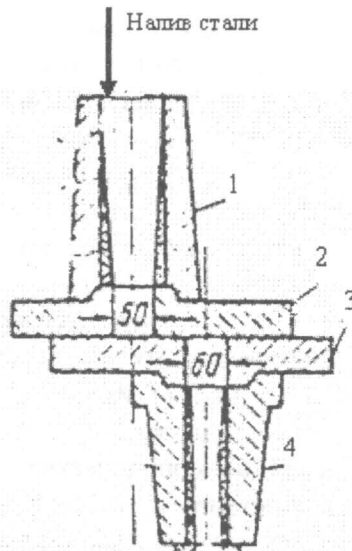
Схема шиберного затвора для бесстопорной разливки стали:
